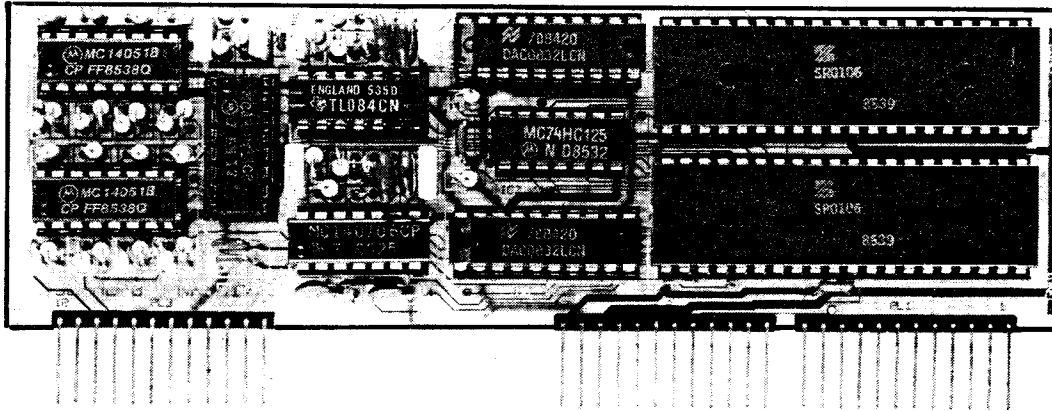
Fertig bestückte Steckkarte SL - M 2 (SVS-System)
